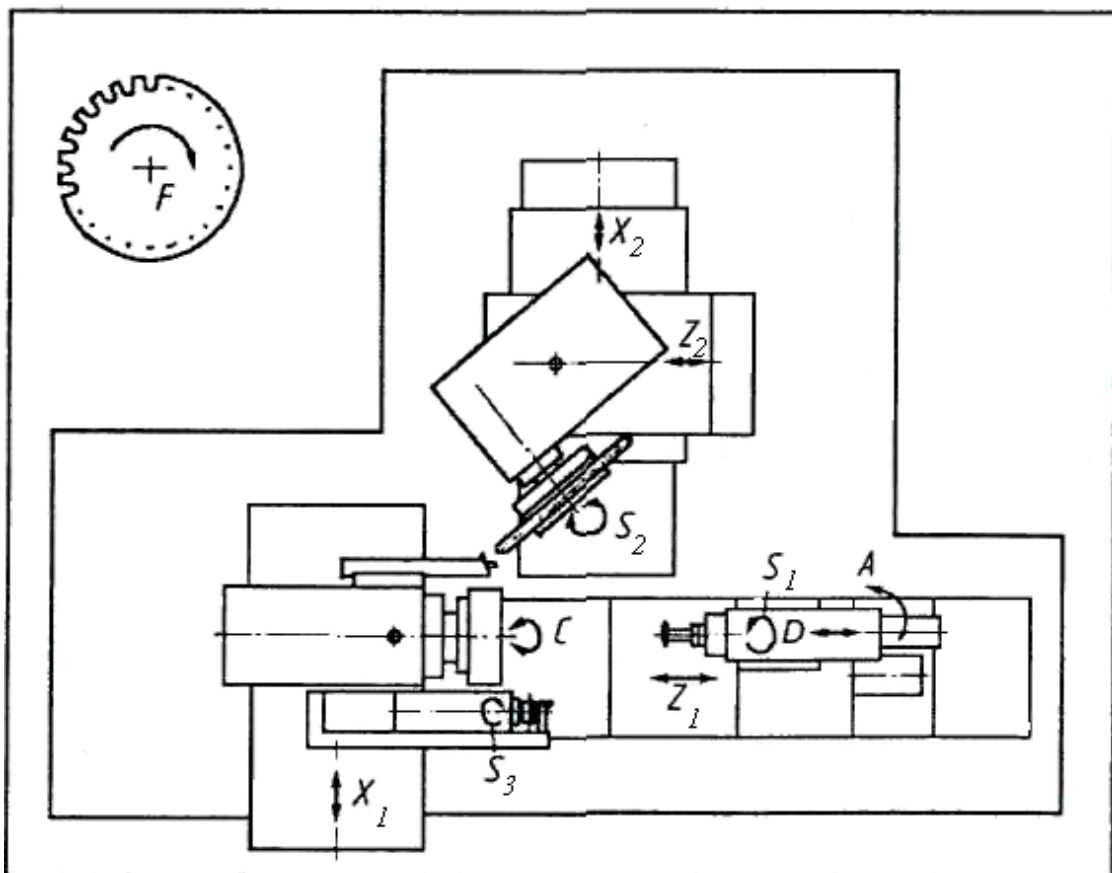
Схема круглошлифовального станка с ЧПУ:
